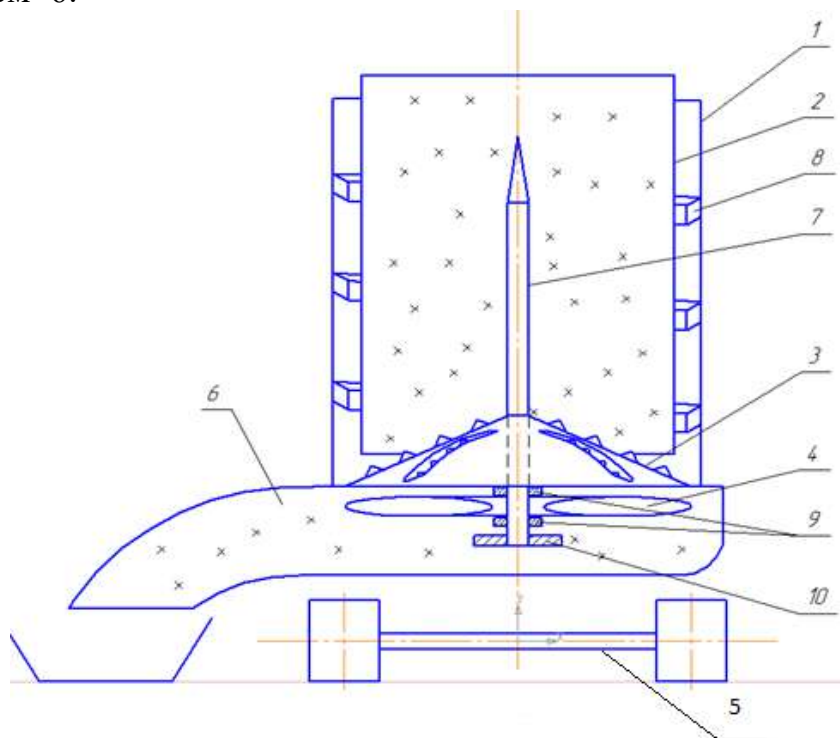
Конструктивно-технологічна схема подрібнювача грубих кормів: 1 – бункер; 2 – рулон; 3 – подрібнюючий робочий орган конусного типу; 4 – лопатеве колесо; 5 – ходова
